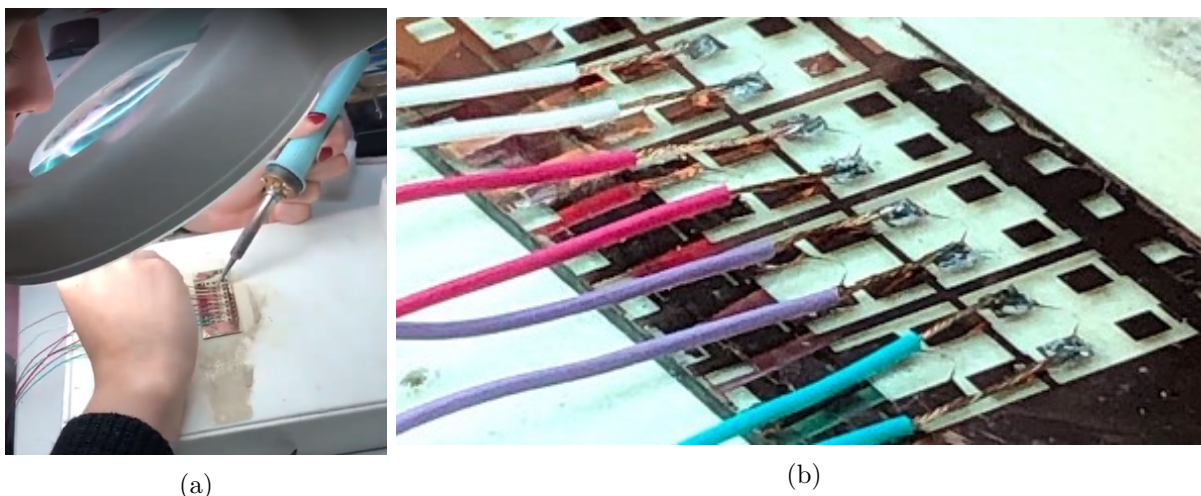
Imágenes tomadas de: (a) el proceso para soldar los cables a los conductores mediante el uso de la lupa y (b) las soldaduras con pasta de estaño.
